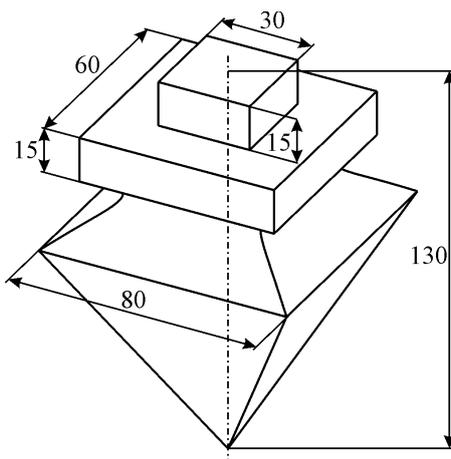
Схема отливки «опорный наконечник стойки конвейера»
